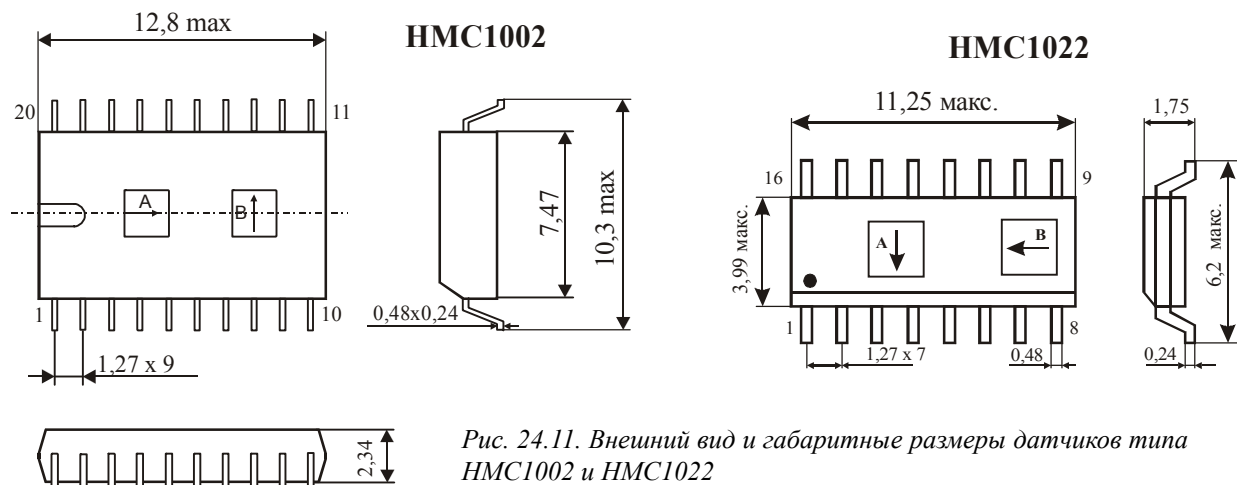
Внешний вид и габаритные размеры датчиков типа HMC1002 и HMC1022
